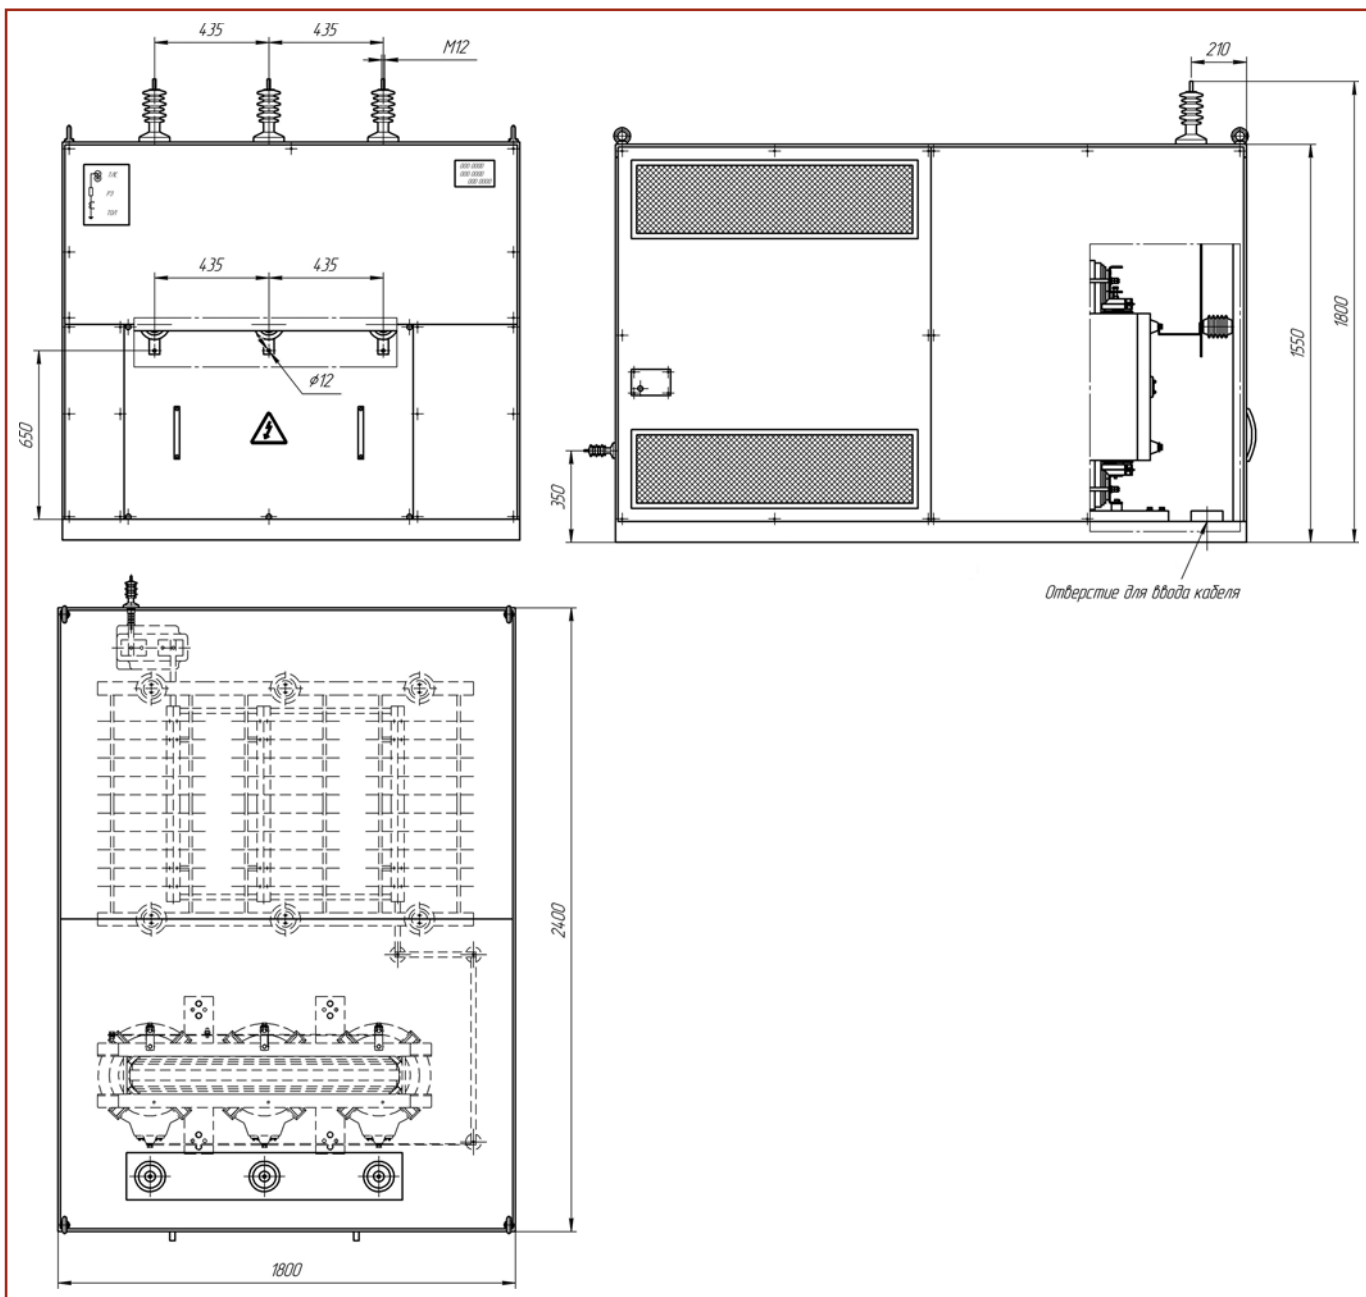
Общий вид устройства КРЗН (30 Ом, 10 кВ) с габаритными размерами
